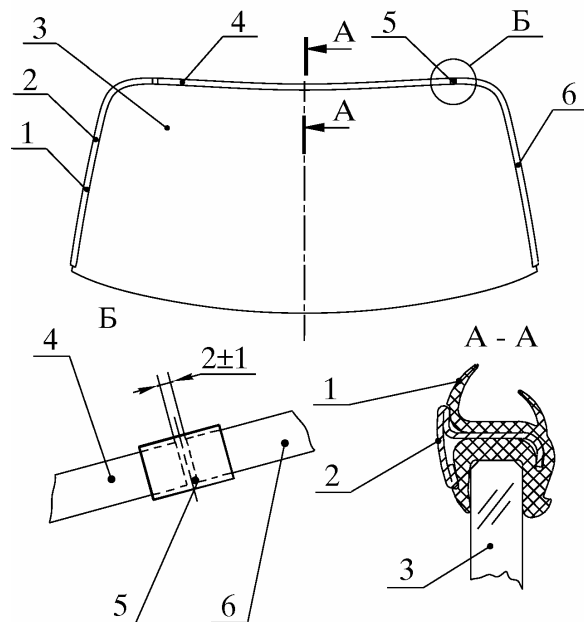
Установка уплотнителя и окантовок стекла задка:
